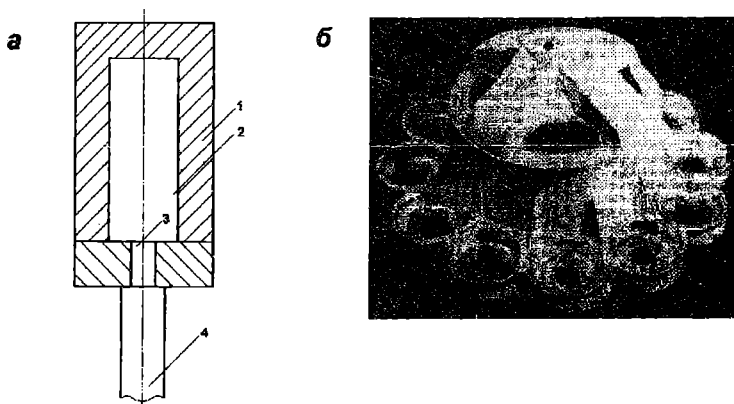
Подвод металла к отливкам: а – нижний подвод из металлопровода через питатель: 1 – форма, 2 – отливка, 3 – питатель, 4 – металлопровод; б – нижний рассредоточенный подвод
